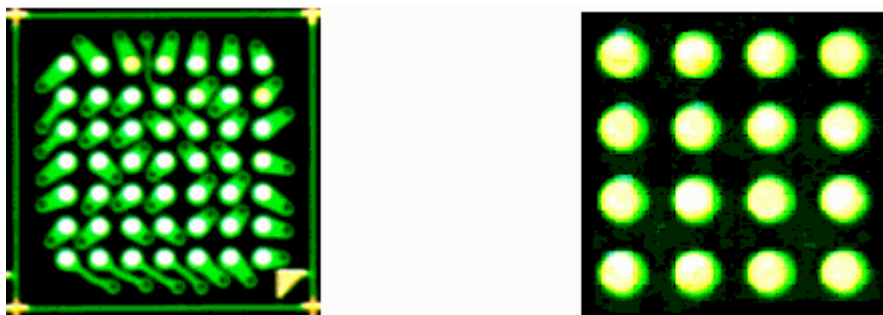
此为手机板上 μ -BGA 之焊垫布局与 COB 安晶与打垫等放大二十倍之实象。
